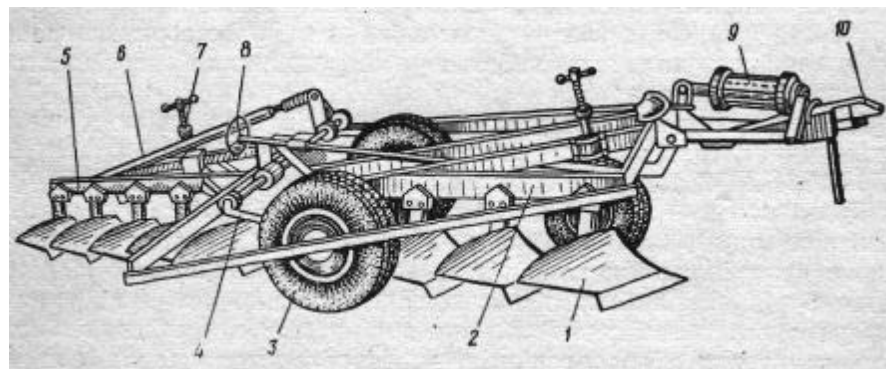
Лемішний плуг-луцильник ППА-10-25: 1 — корпус; 2 — секція рами; 3 — колесо; 4 — вісь; 5 — штанга; 6, 7 — регулятори глибини; 8 — довантажувач; 9 — гідроциліндр; 10 — причіпний пристрій
